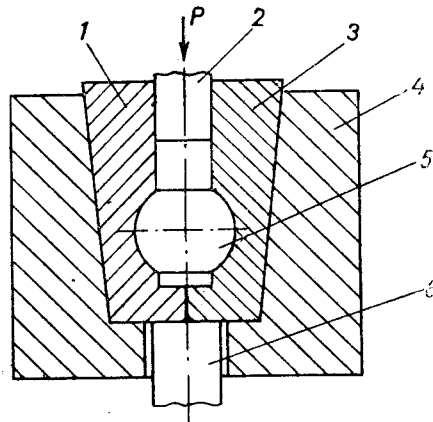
Закритий штамп для фрикційного гвинтового преса:
